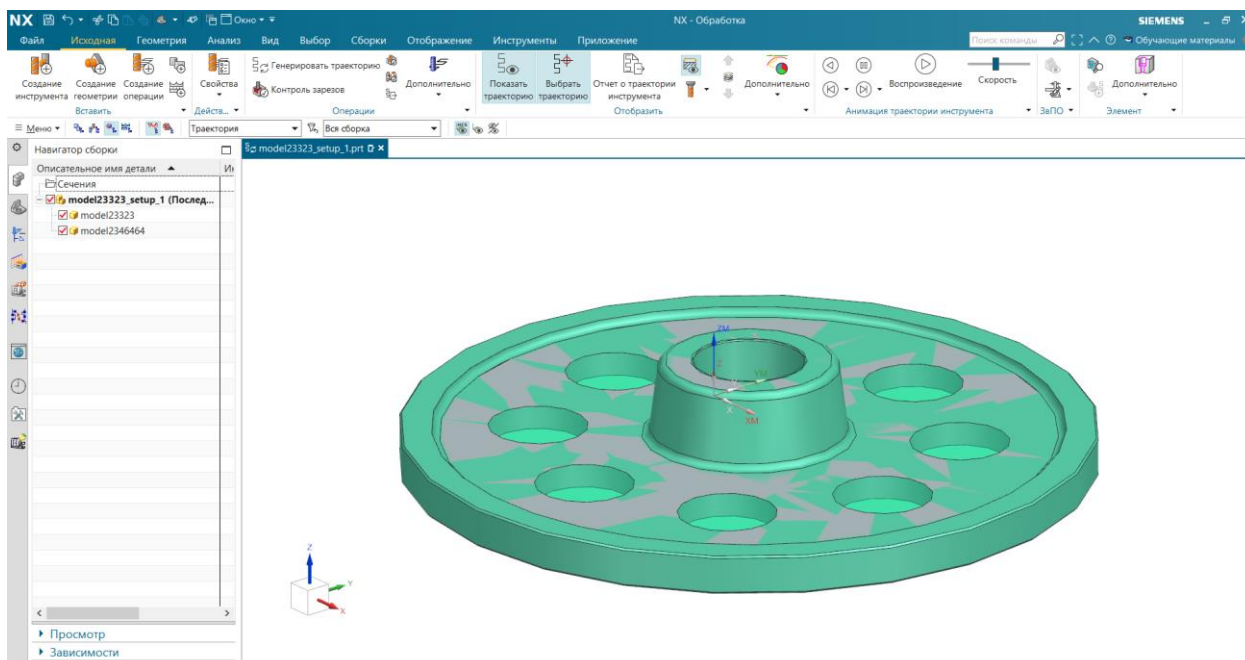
Поєднання 3D-моделей деталей та заготовки
